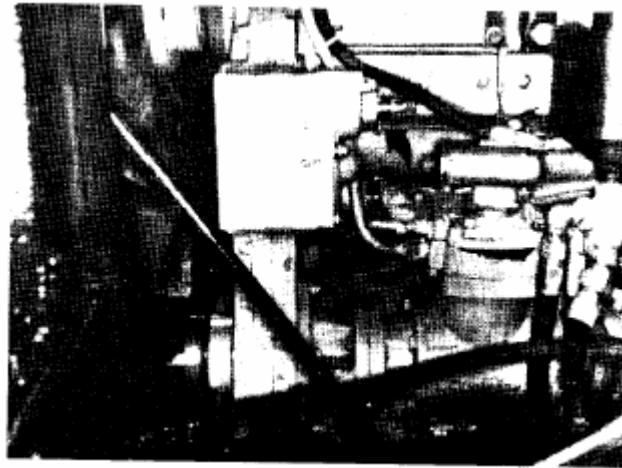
(К11919). Конструкция устройства для прокручивания двигателя - КТ/КТА19.
